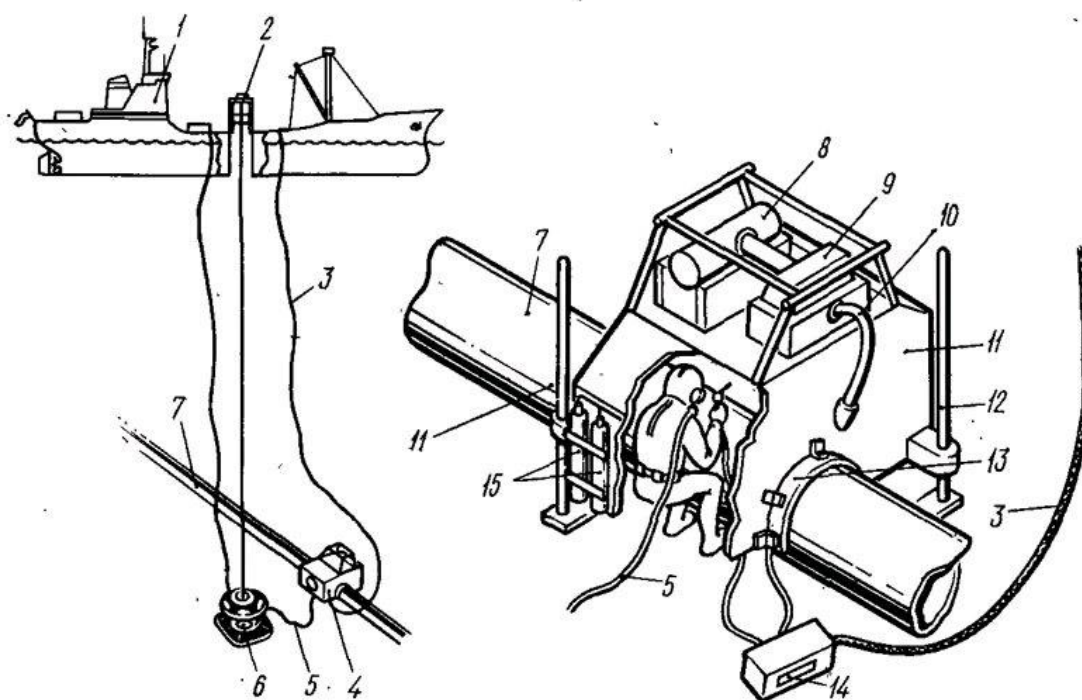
Схема выполнения «мокрой» сварки под водой
